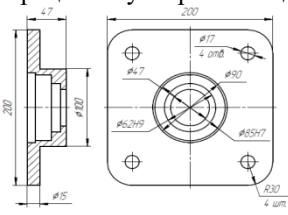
Корпус підшипника АП-6.03.501 Рис. 2. Твердотільна модель
